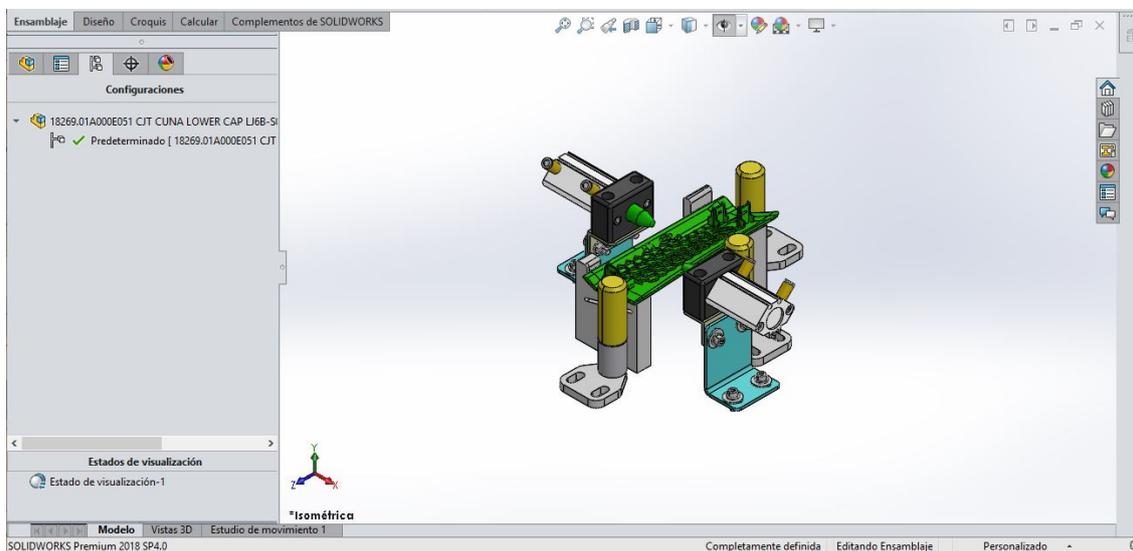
Diseño cuna LOWER END PNL STRIP FINAL
